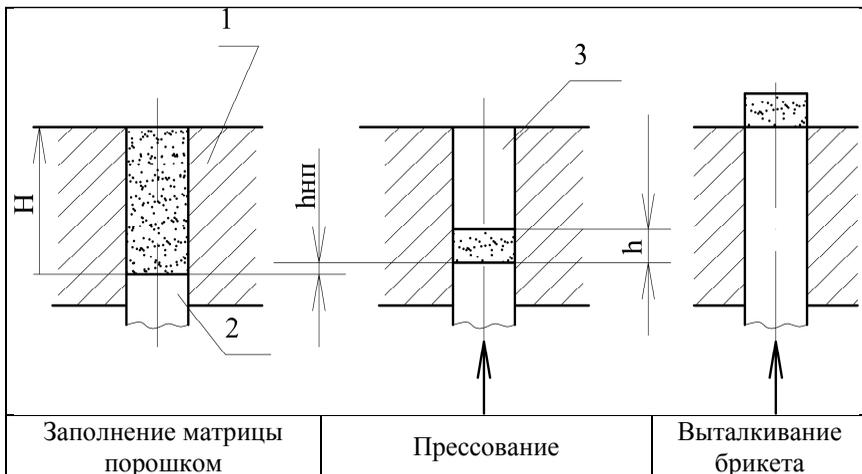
Схема пресс-формы с неподвижной матрицей для двустороннего прессования:
